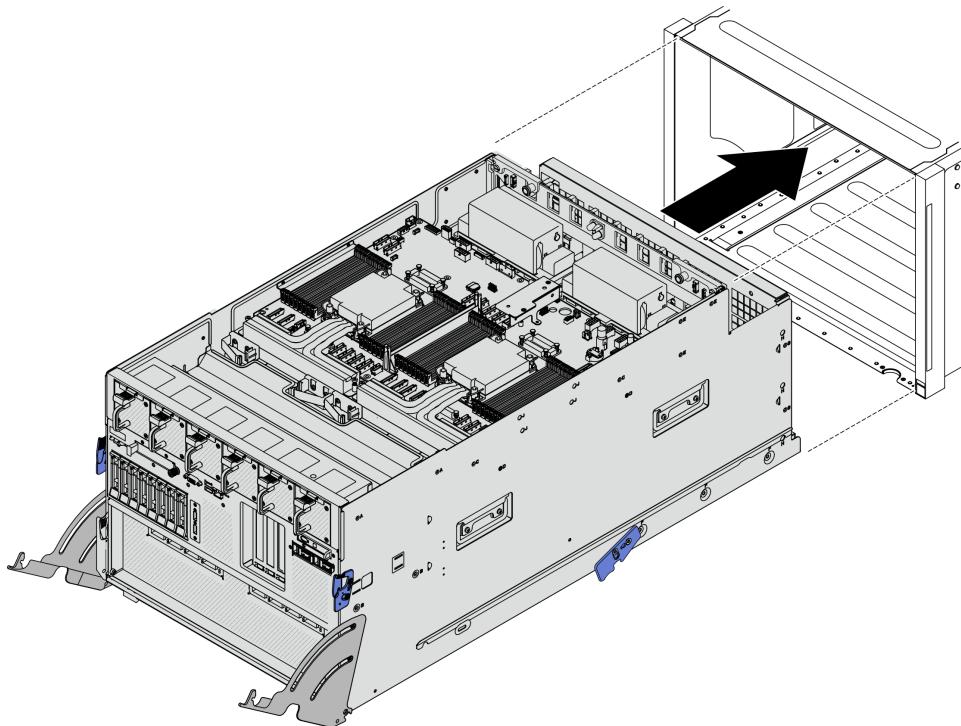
Mise en place (en poussant) de la navette système en position d'arrêt
